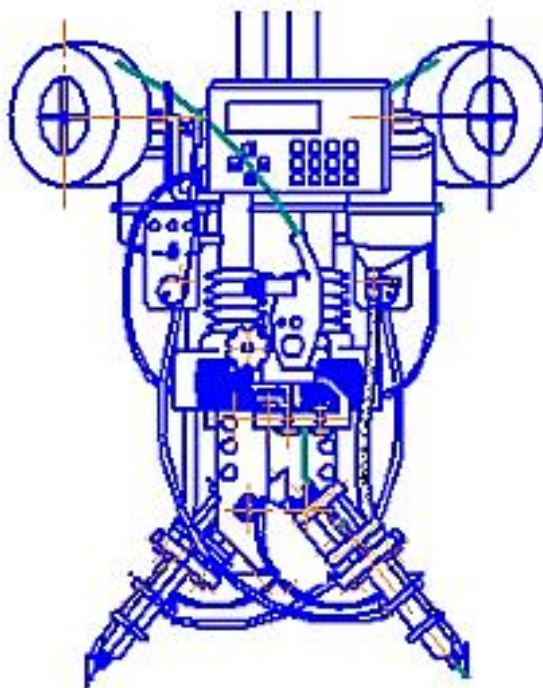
Ескіз зварювального автомат АДГ-630
